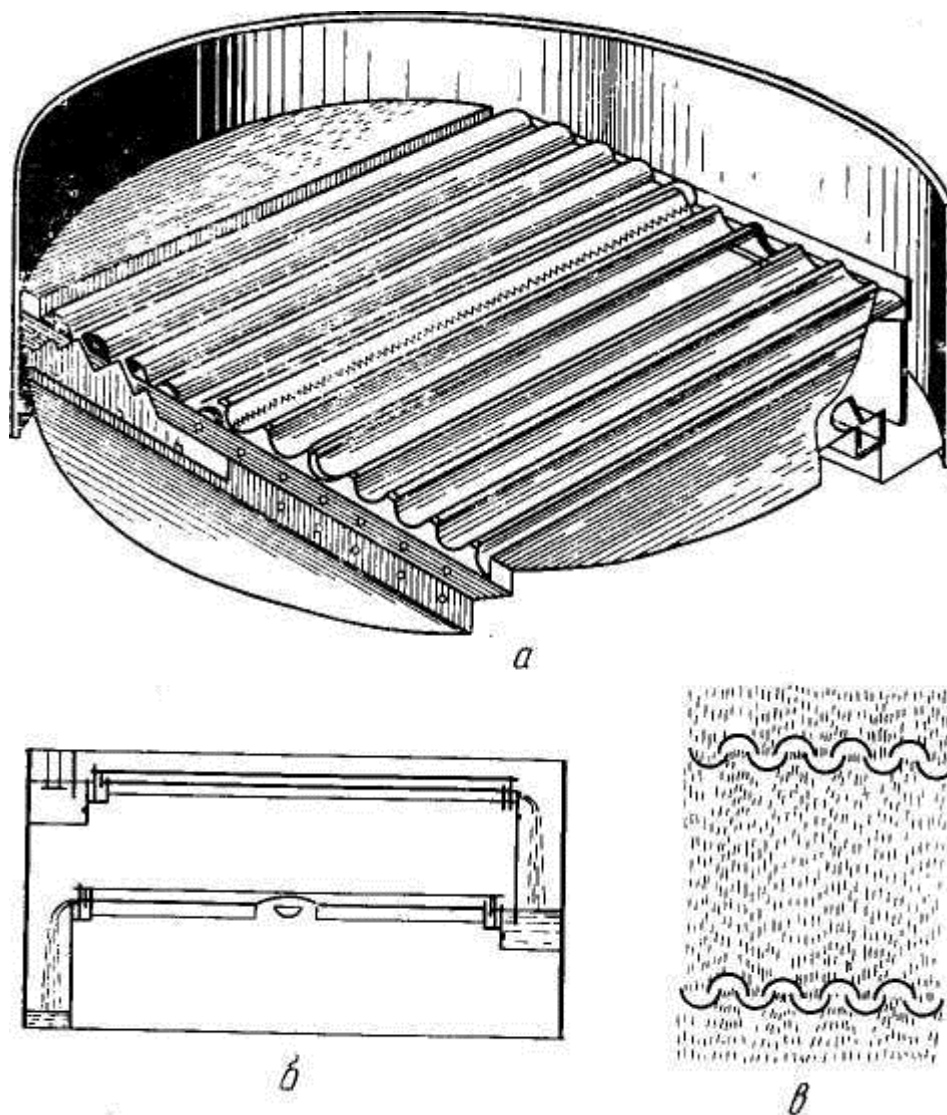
Тарілка з жолобчастим ковпачками: а - загальний вигляд; б - поздовжній розріз; в - схема роботи тарілки
